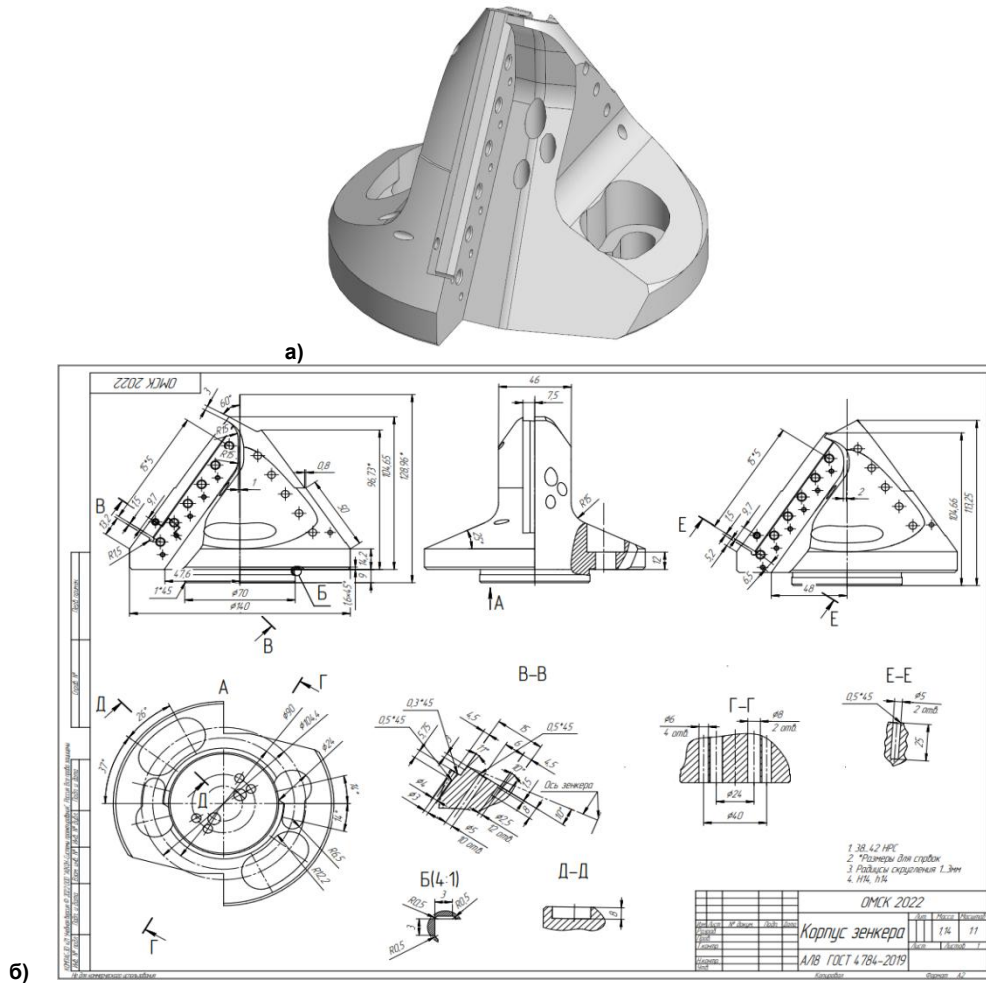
Корпус Зенкера: а – 3D-модель, б – чертёж детали
